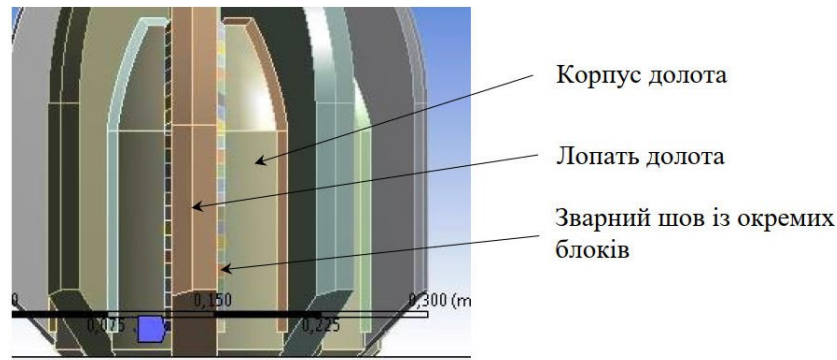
Схема моделювання зварних швів приварювання лопаті до корпусу долота
